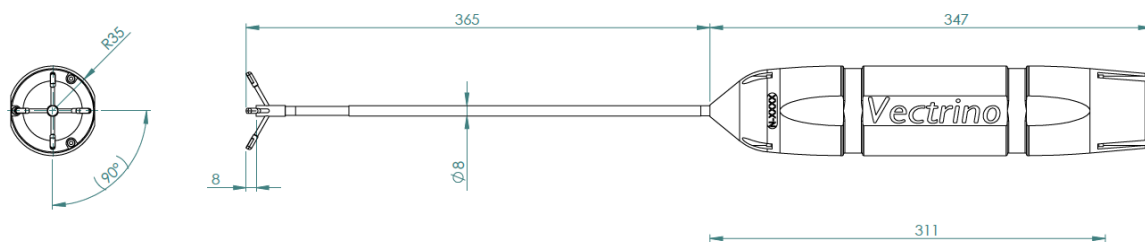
Pormenor construtivo do Vetrino Plus com downlooking (adaptado de Nortek (2009))
